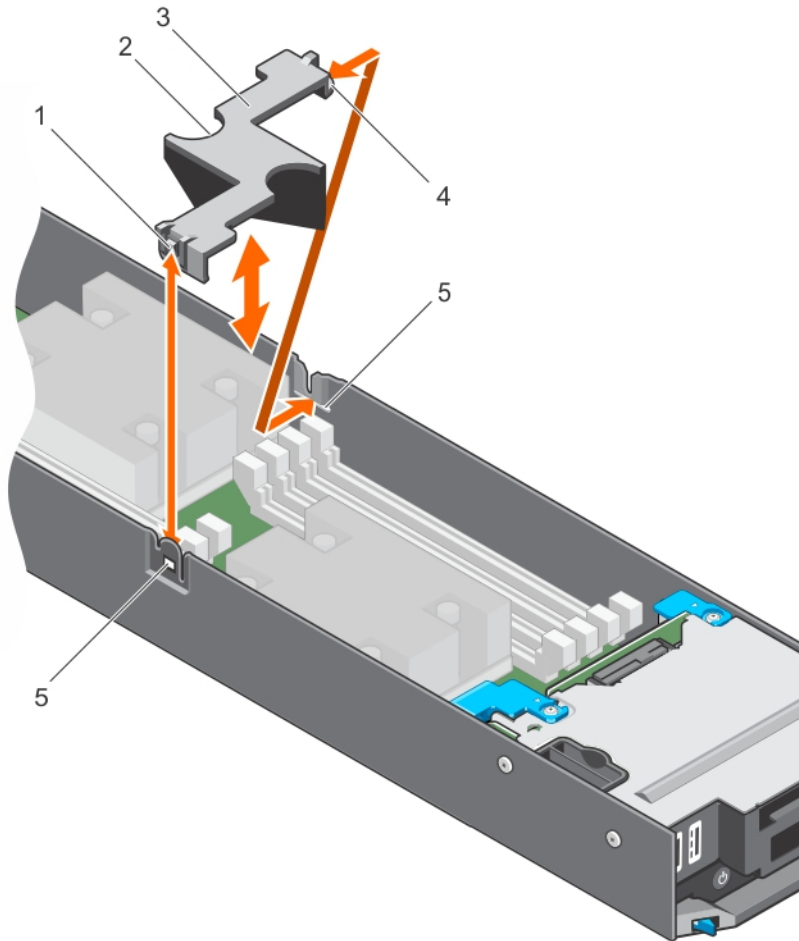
Extracción e instalación de una cubierta de refrigeración
